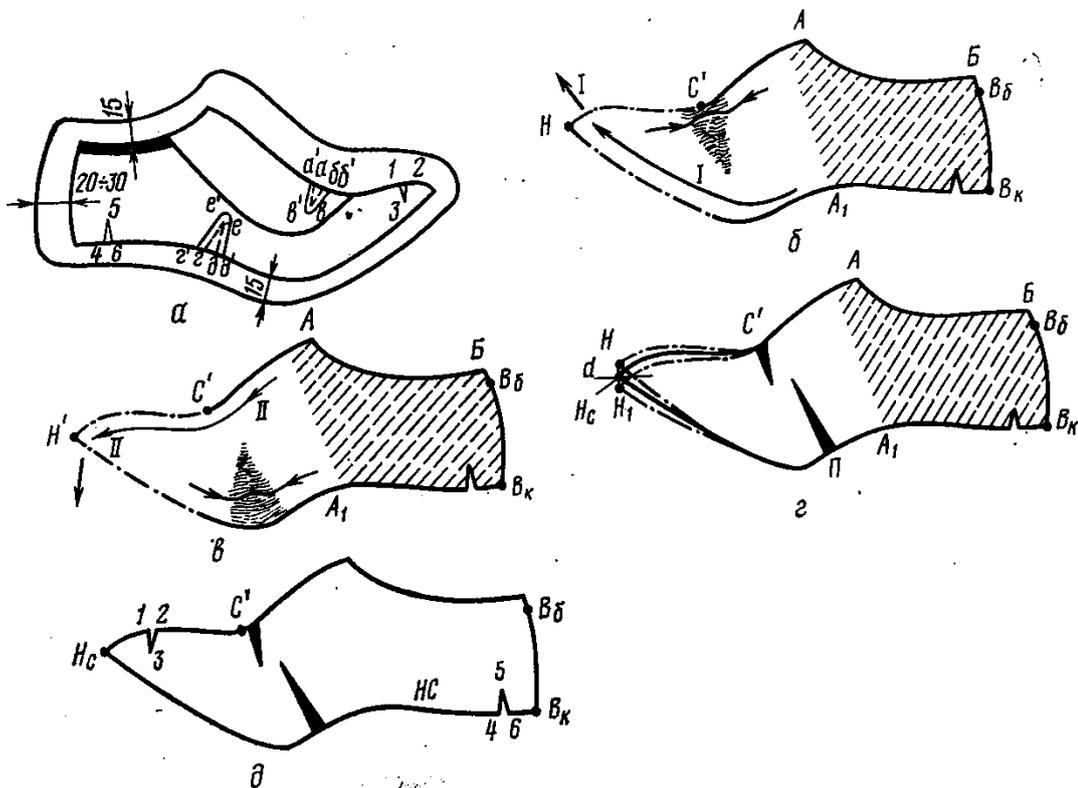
Этапы подготовки бумаги для получения условной развертки боковой поверхности колодки
